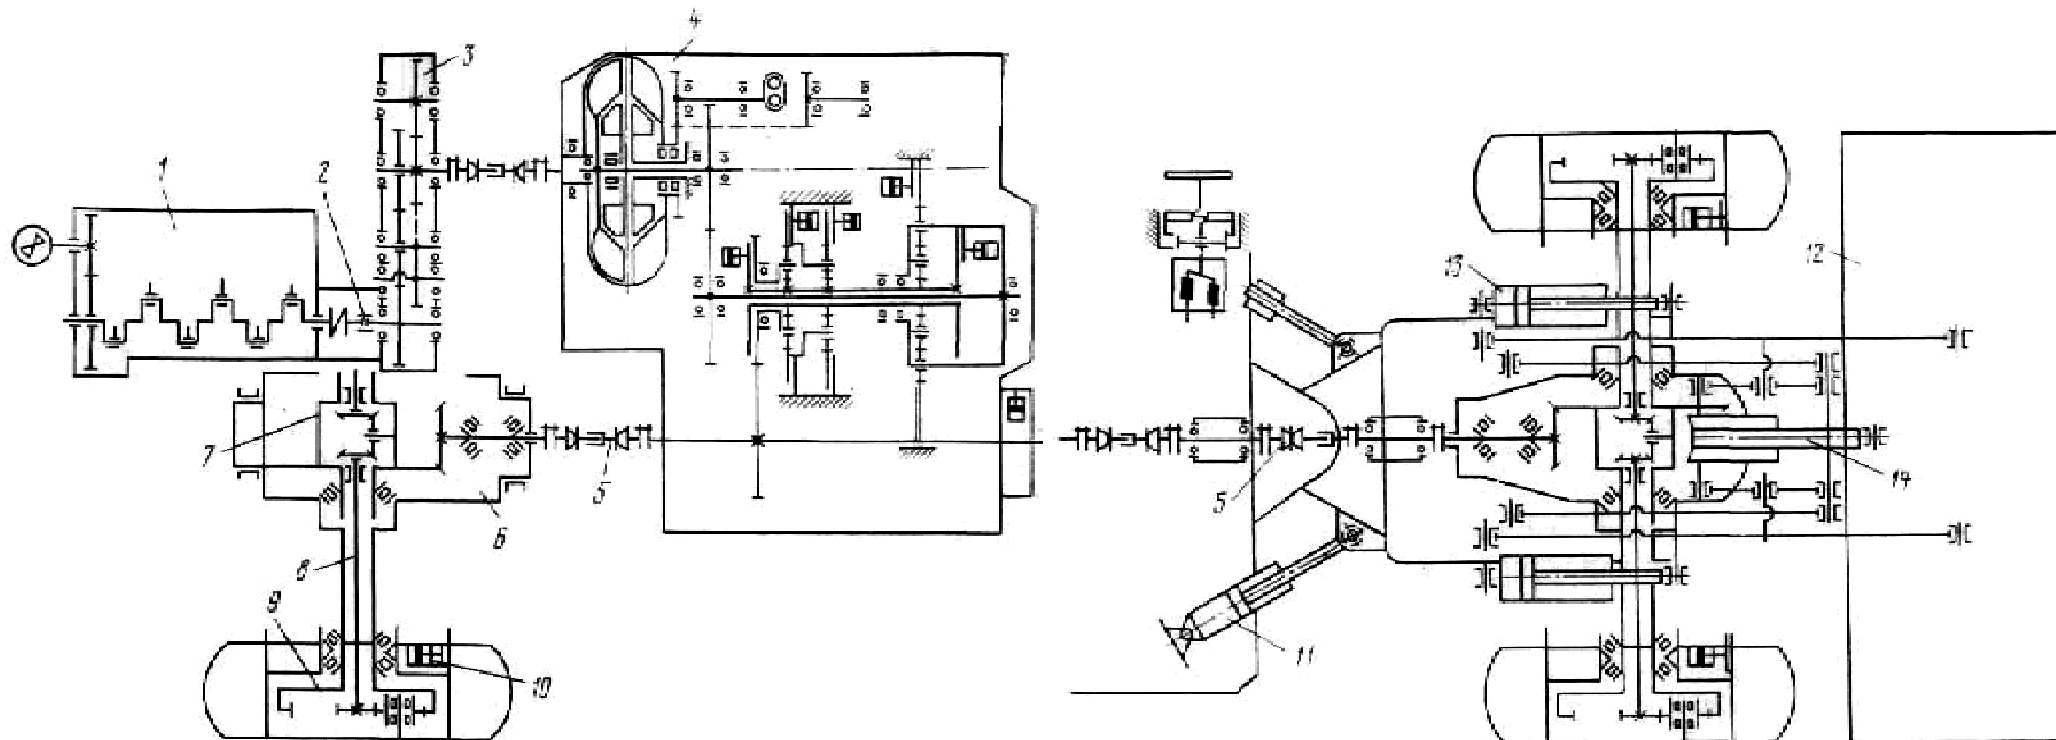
Кинематическая схема погрузочно-транспортной машины ПД-5: 1 — двигатель; 2 — демпферное соединение; 3 — редуктор согласующий; 4 — гидратрансформатор с коробкой передач планетарного типа; 5 — карданный вал ведущего моста; 7 — дифференциал; 8 — полуось; 9 — планетарный колесный редуктор; 10 — тормоз рабочий; 11 — гидроцилиндр поворота машины; 12 — ковш; 13 и 14 — гидроцилиндры соответственно подъема стрелы и поворота ковша
